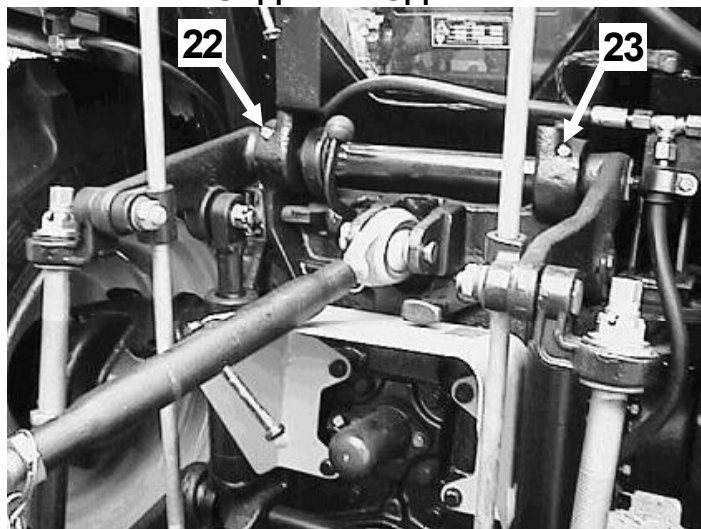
ТСП – два пункта смазки 22 и 23- масленки подшипников скольжения, расположенных в корпусе вала плечей гидравлического подъемника. Смазку производить путем 4-5-кратного нажатия рычага масленки.
